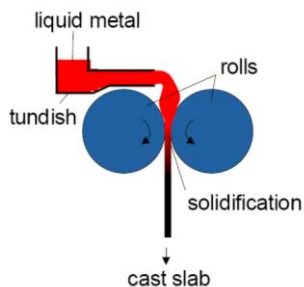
Representación esquemática de la máquina de colada de doble tambor diseñada por Hazelett Sr.
